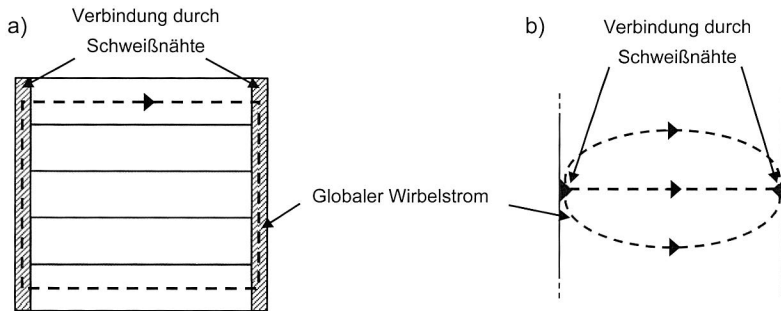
Durch zwei Paketierschweißnähte gebildete Wirbelstrombahnen; a) Schnittansicht, b) Draufsicht
